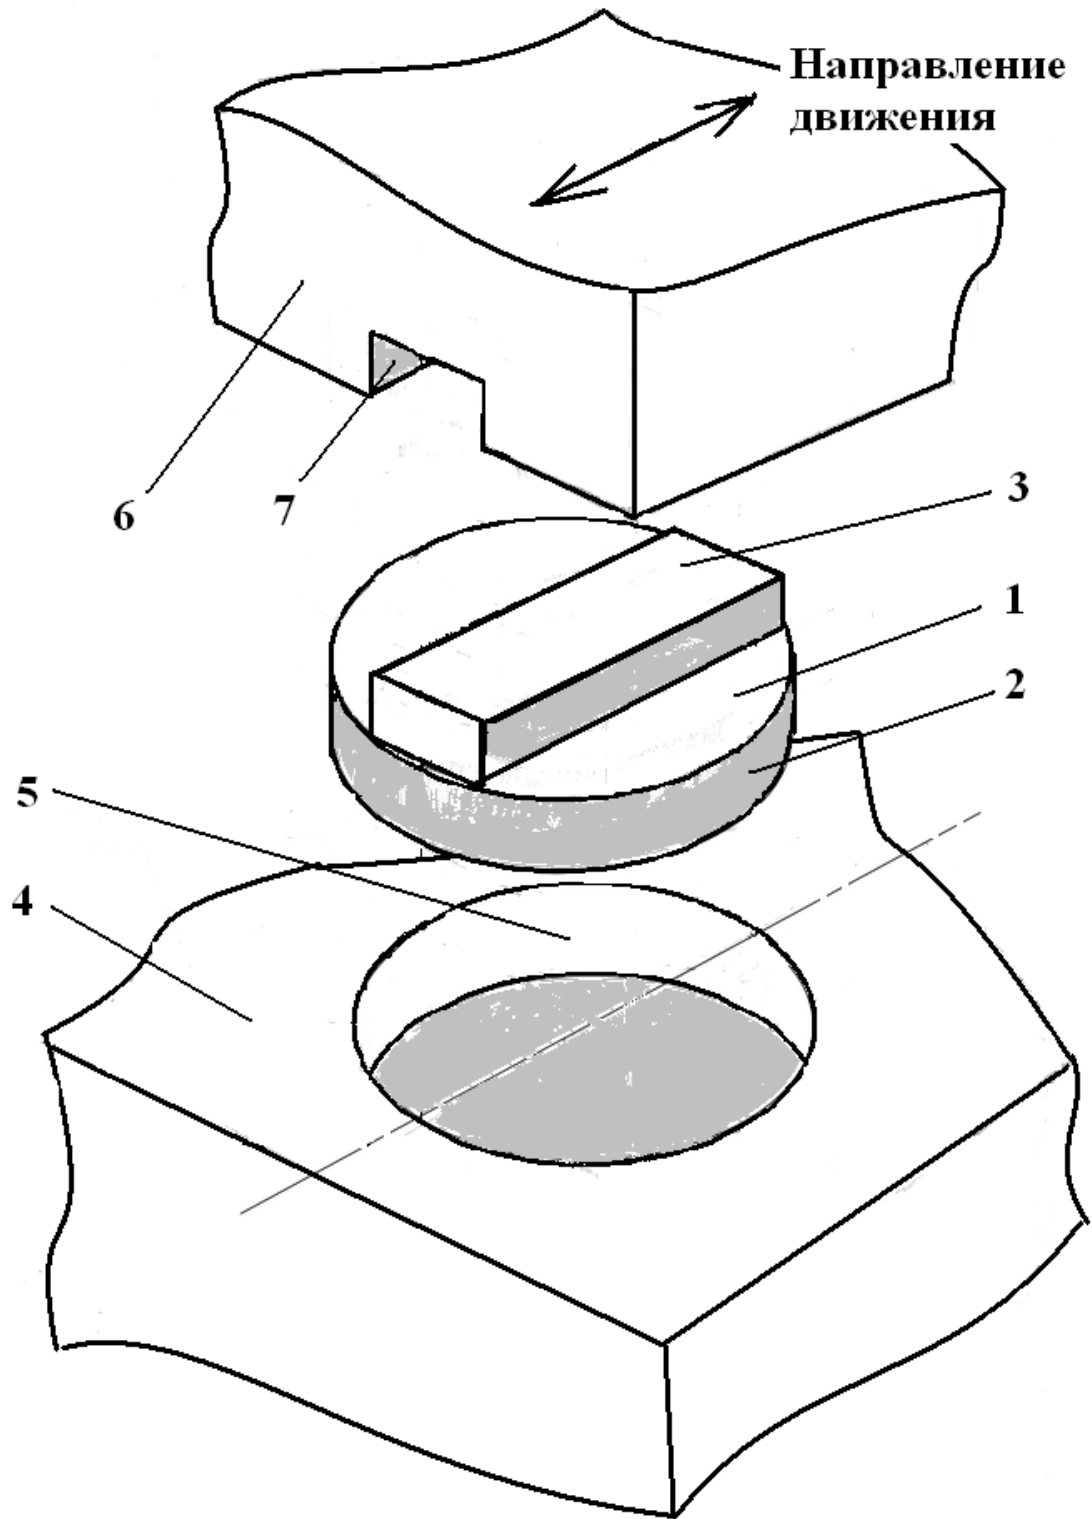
Дисконая направляющая выносного корпуса подшипника
